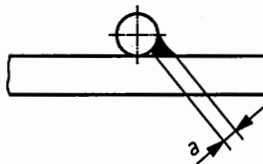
zeigt ein Beispiel für einen Überlappstoß. Die Bilder 2 und 3 zeigen Beispiele für Kreuzungsstöße. Die Länge der Schweißnaht,  $l$ , und die Kehlnahtdicke,  $a$ , sind von der Anwendung abhängig und müssen der WPS entsprechen.
